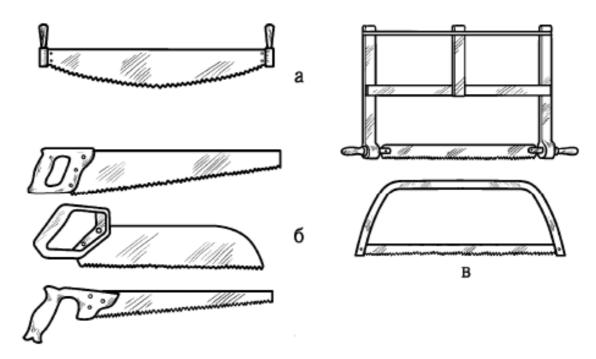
Инструмент для пиления: a — двуручная пила;  $\delta$  — ножовки;  $\epsilon$  — лучковые пилы 5. Инструмент для строгания и придания заготовке соответствующих формы и профиля (рис. 31). Сюда входят шерхебель, использующийся для грубой острожки древесины; различные рубанки, которыми обрабатывают заготовку после острожки; для более тонкой работы (выравнивания поверхности) предназначен фуганок; для строгания выпуклых и вогнутых поверхностей применяют особый рубанок — горбач; чтобы выполнить желобки, различные по радиусу, ширине и глубине, работают галтелем. Фальцгебель и зензубель незаменимы, если нужно выбрать фальцы и четверти (если фальцы и четверти выбраны стамеской, их зачищают зензубелем); калевка — инструмент, которым пользуются для профильной обработки кромок.
